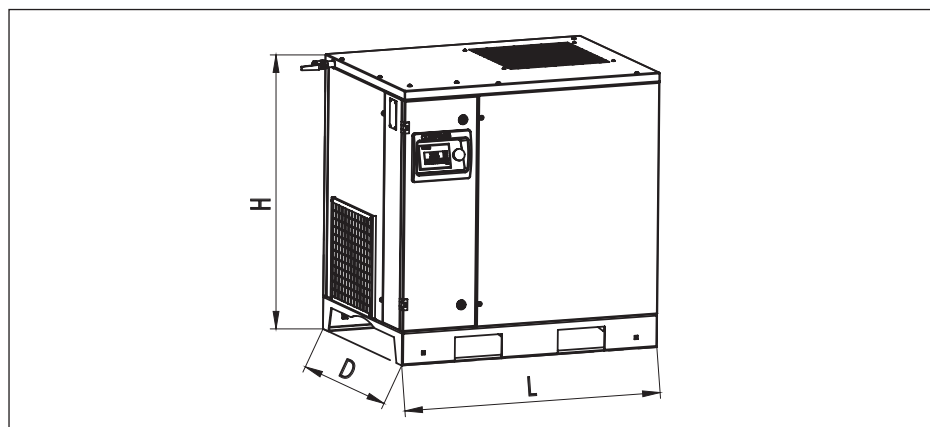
Размеры компрессора F5,5.. – F22.
